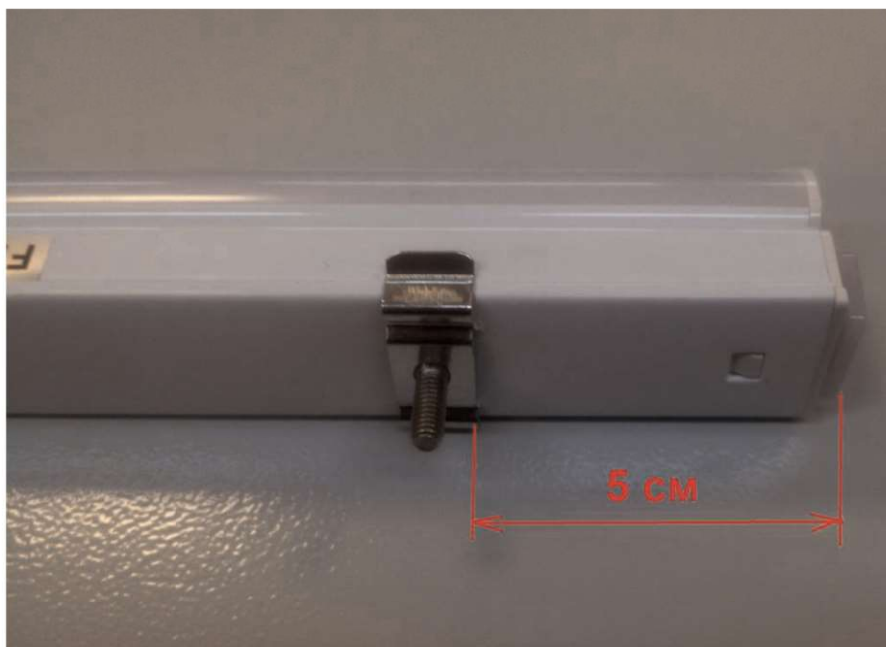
Установка крайнего пружинного держателя.
